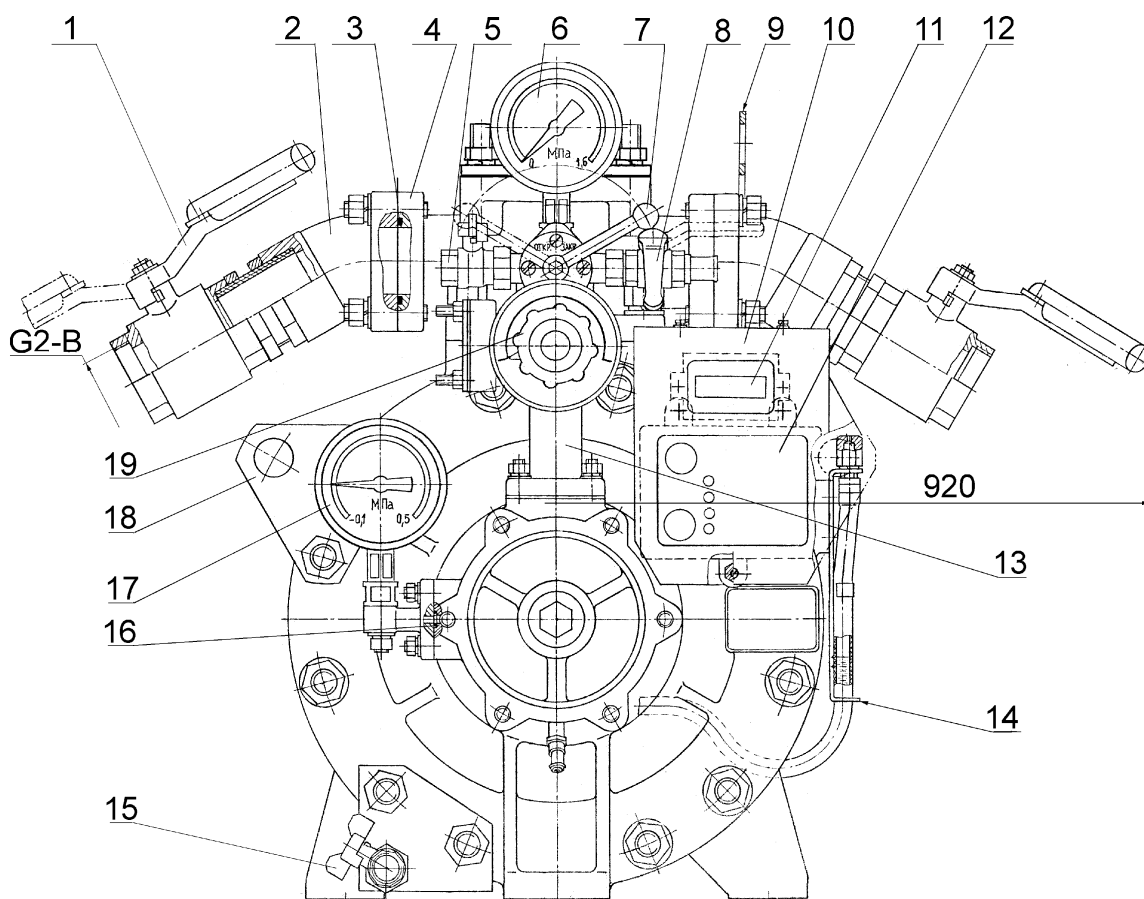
Насос НЦПВ-20/200 (вид со стороны всасывающего патрубка).
